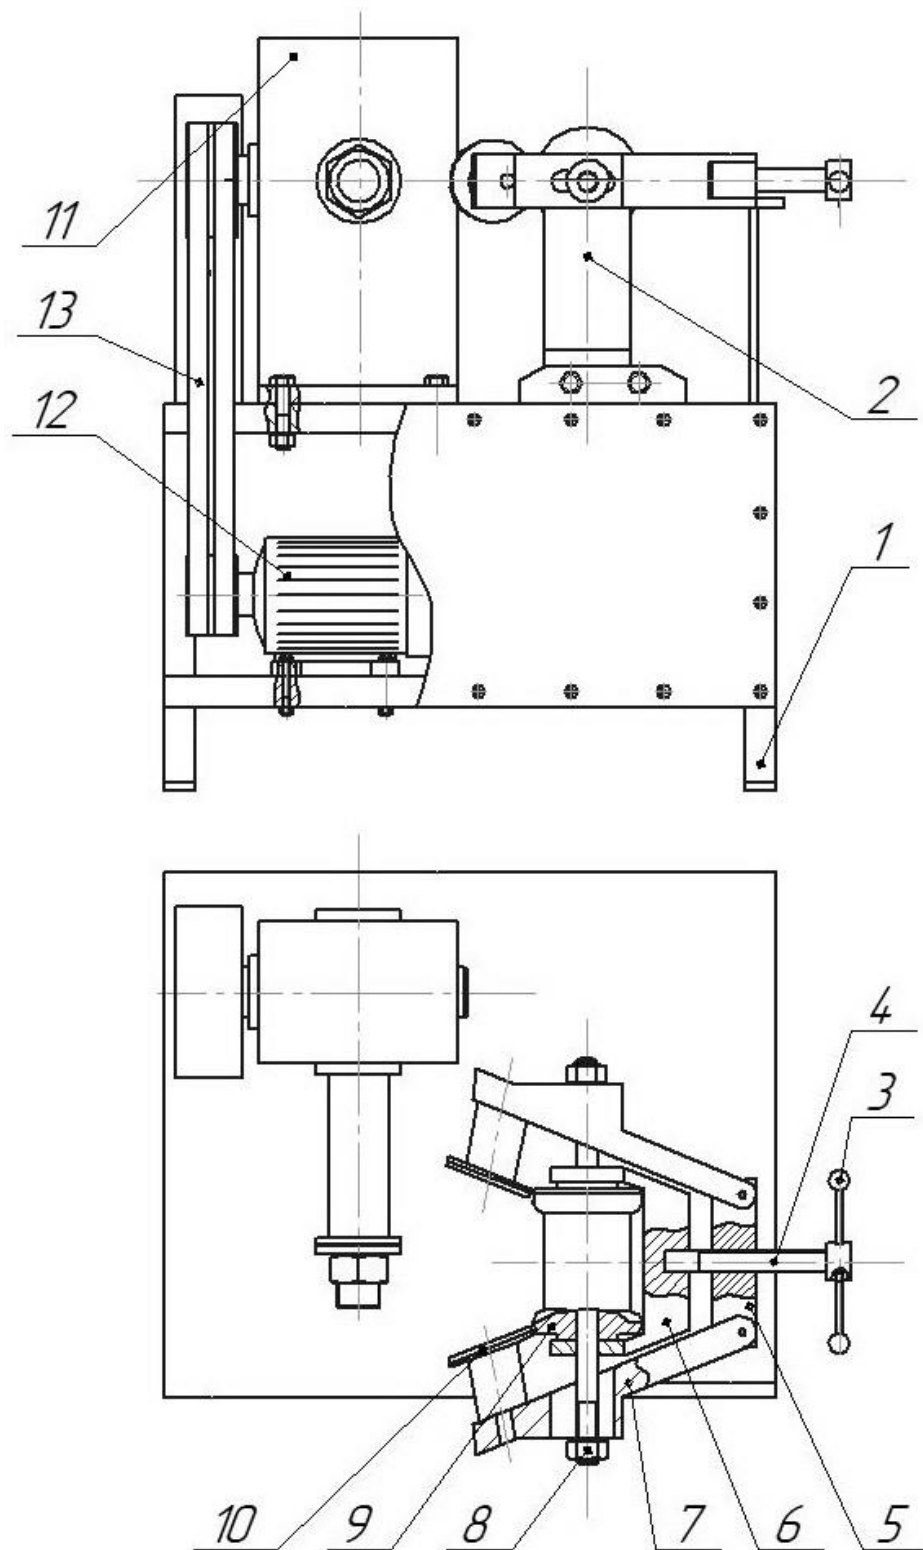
Стенд для прокатки штампованих дисків:
